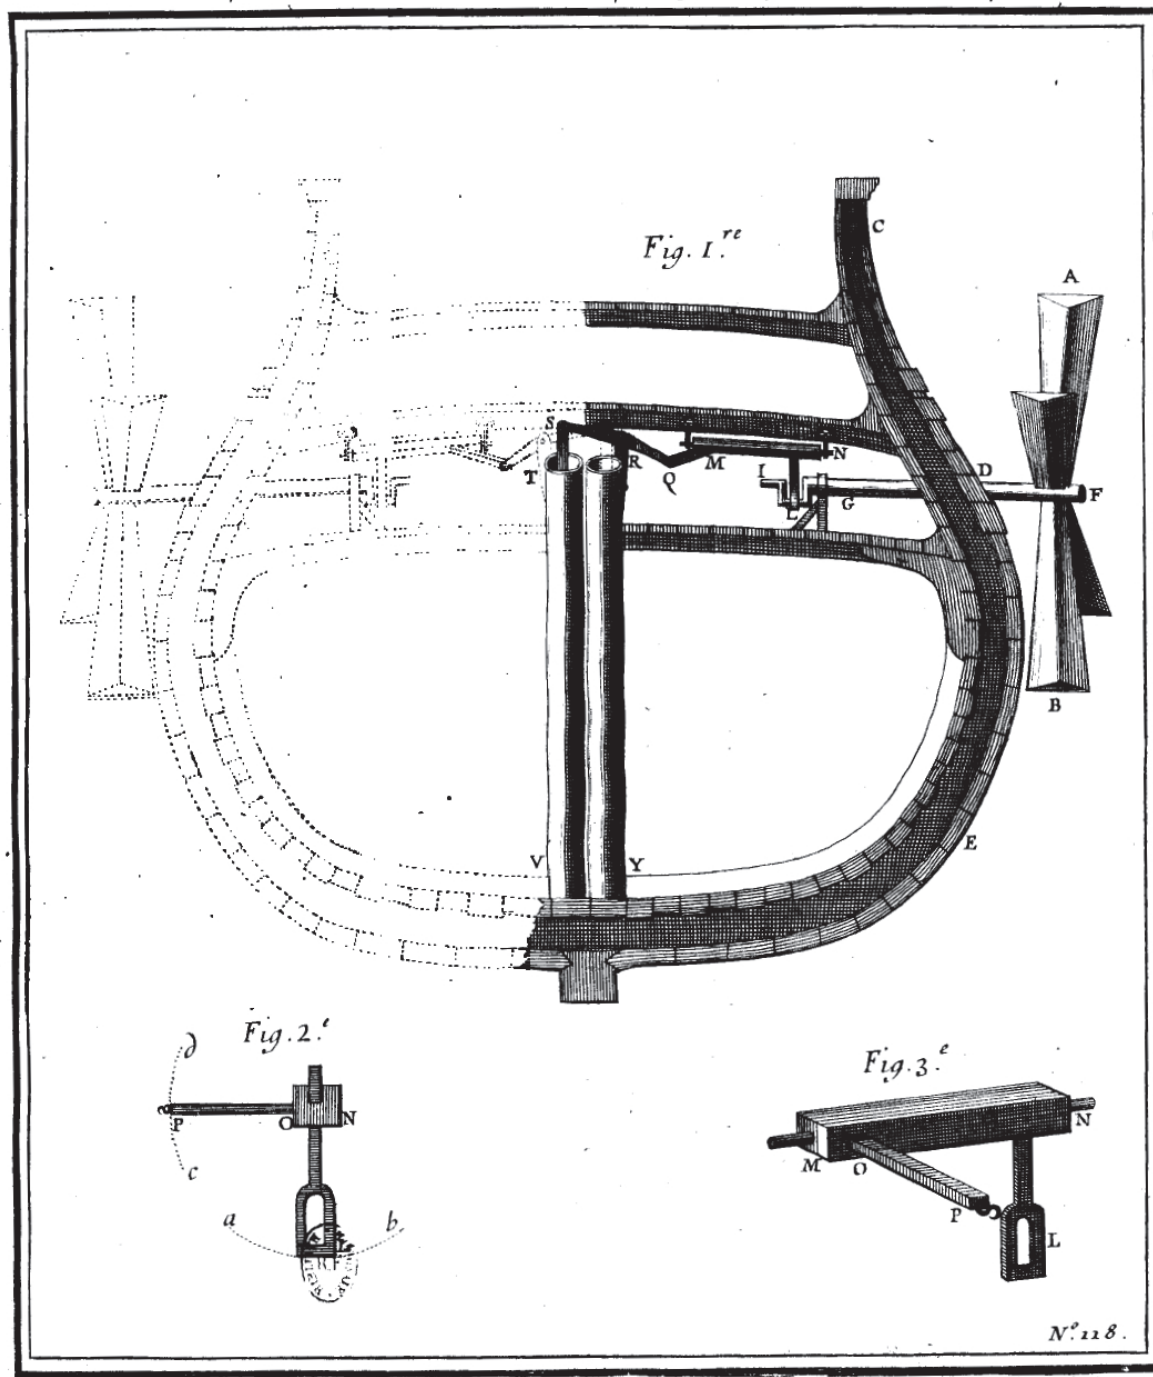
Moulin à faire jouer des pompes de Du Quet (Tome 2 des Machines, p. 136)
